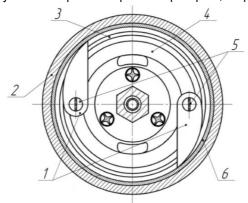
Центробежный масляный фильтр с дозатором присадки: 1 – графитовые щетки; 2 – корпус; 3 – ротор; 4 – крышка; 5 – винты; 6 – колпак
